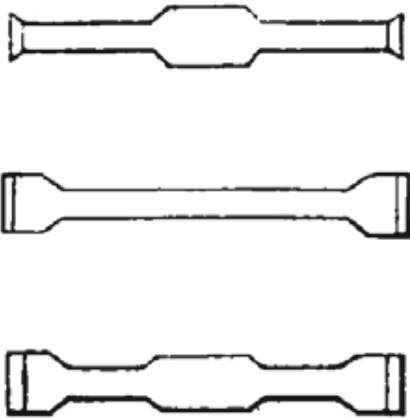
| Verschiedene Arten von Stäbchen (Grundriss)
